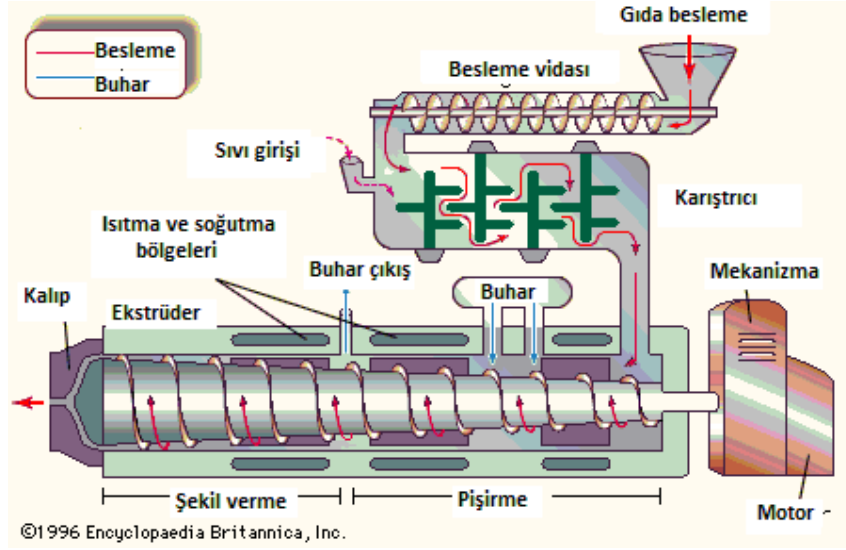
Ekstrüzyon işleminde kullanılan tek vidalı ekstrüder
